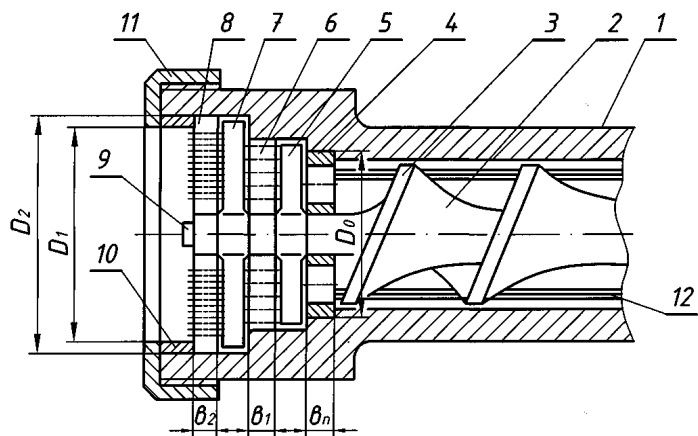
Схема режущего механизма волчка: 1 – корпус; 2 – шнек; 3 – ребра; 4 – решетка подрезная; 5, 7 – ножи подвижные; 6 – решетка приемная; 8 – решетка выходная; 9 – палец; 10 – кольцо упорное; 11 – гайка; 12 – ребра продольные; b_n – толщина подрезной решетки 4; b_1 – толщина приемной решетки 6; b_2 – толщина выходной решетки 8; D_0 – наружный диаметр подрезной решетки 4; D_1 – наружный диаметр приемной решетки 6; D_2 – наружный диаметр выходной решетки 8
